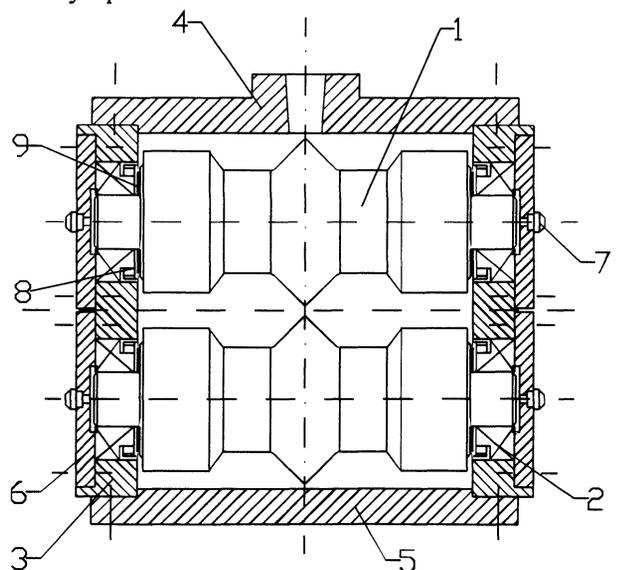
Конструкция делительного устройства фирмы «Ferrco» (Англия): 1 – делительные ролики; 2 – подшипники; 3 – боковые стойки корпуса; 4 – крышка корпуса; 5 – основание корпуса; 6 – торцовые крышки; 7 – масленки; 8 – защитные кольца; 9 – прокладки
